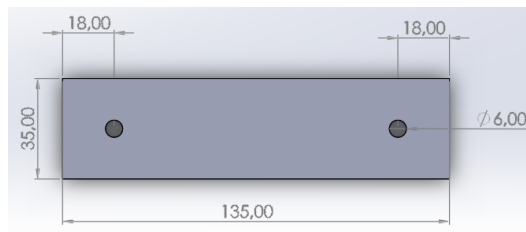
Esboço de provete para ensaio Bearing com dois furos [54]
